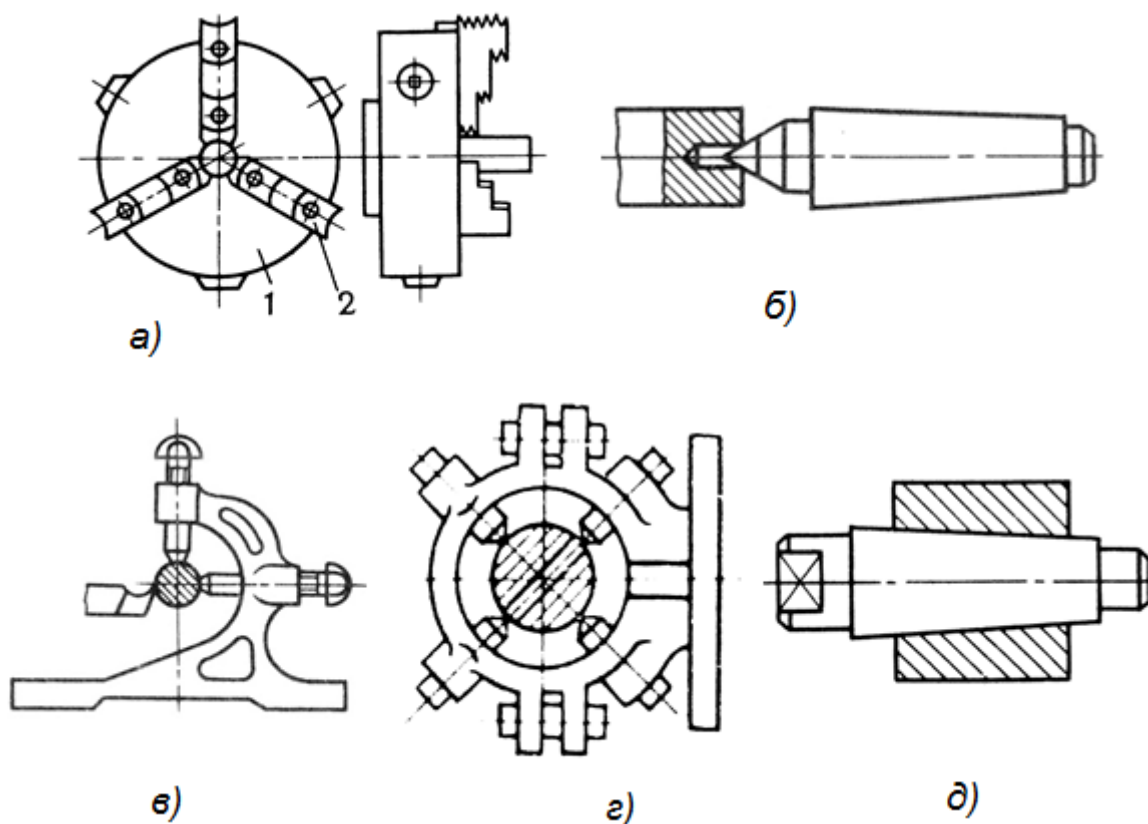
Приспособления для закрепления заготовок на токарных станках:
